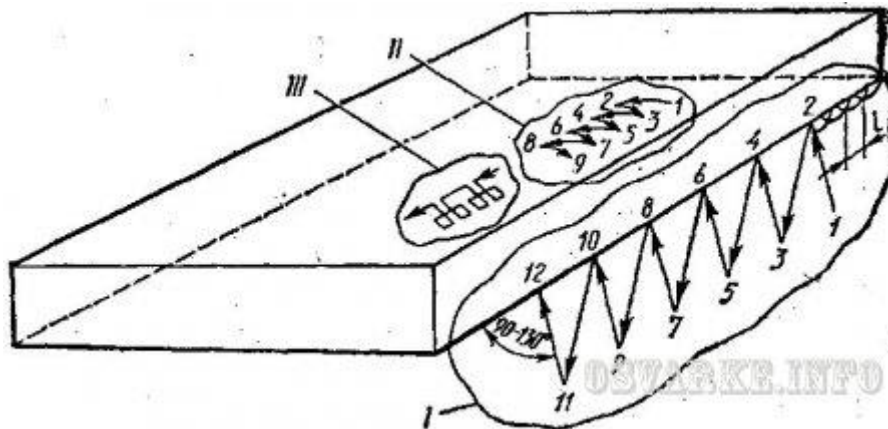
Схема наложения узких валиков в потолочном положении: I - лесенкой, II - полумесяцем, III - обратнопоступательно, 1 - диаметр закристаллизовавшейся капли металла
